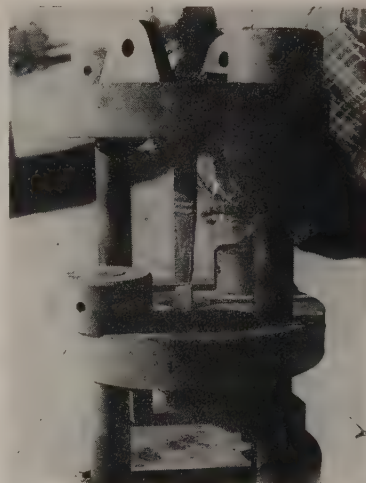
Essais de traction sur barreaux de prélèvement de soudure.
